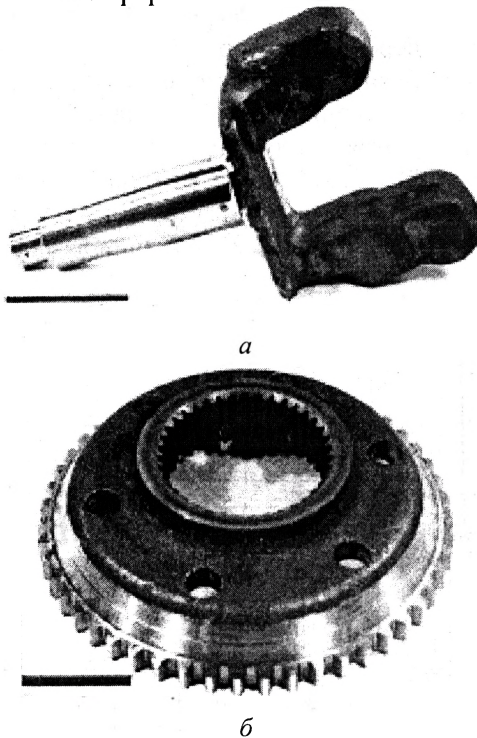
Детали МАЗ, подвергаемые управляемой прерывистой закалке: а — кулак поворотный, б — ступица колесной передачи
